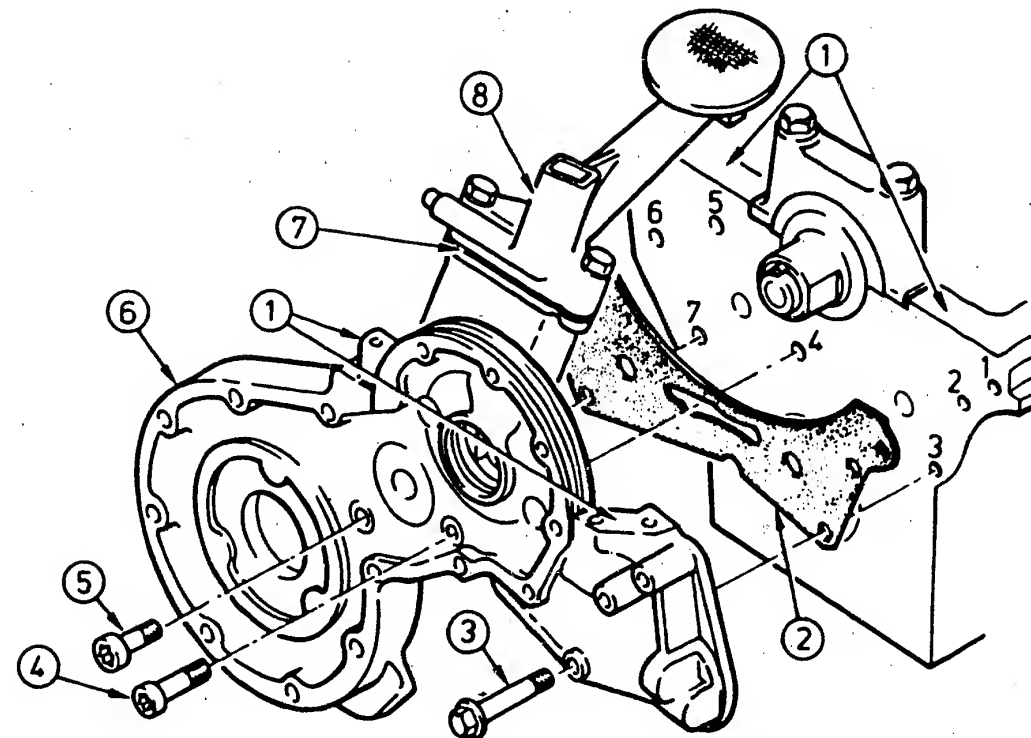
Teile der Ölpumpe am Dieselmotor: 1 Flansch-Dichtflächen – 2 Dichtung – 3 Sechskantschrauben an Pos. 1, 2 und 3 – 4/5 Vielzahn-Inbusschrauben an Pos. 4, 5 und 6, 7 – 6 Ölpumpe mit Gehäuse – 7 Dichtung – 8 Ölansaugrohr mit Sieb und Druckreguliertventil.
